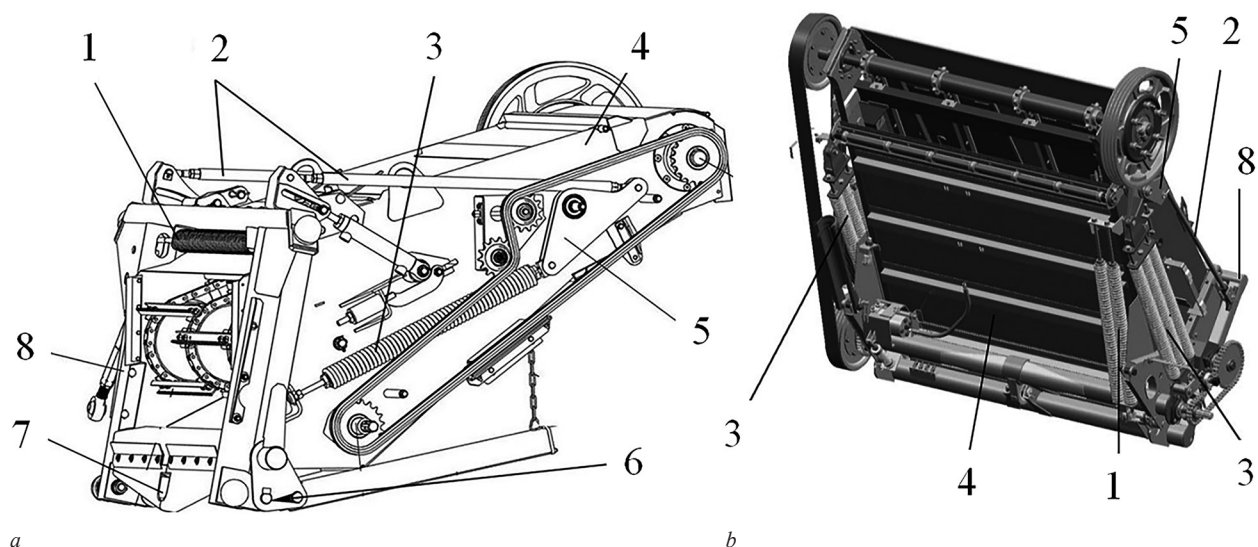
Пружинно-рычажные механизмы уравнивания комбайнов: а — КЗС-10К; б — РСМ-142 АСРОС;
